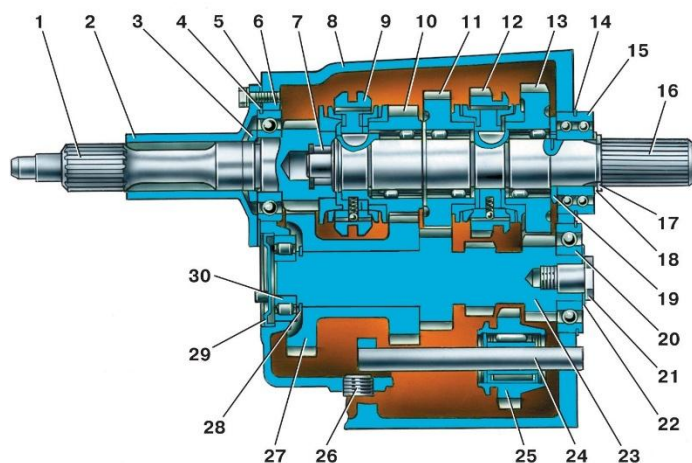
Коробка передач, синхронизированная частично: 1 – картер;
